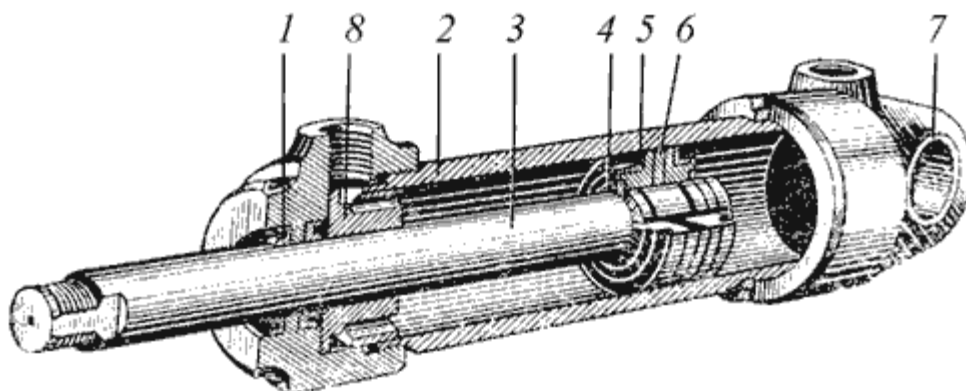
Гидроцилиндр: 1 - грязесъемник; 2 - гильза; 3 - шток; 4 - стопорное кольцо; 5 - манжета; 6 - поршень; 7 - проушина; 8 - грундбукса
